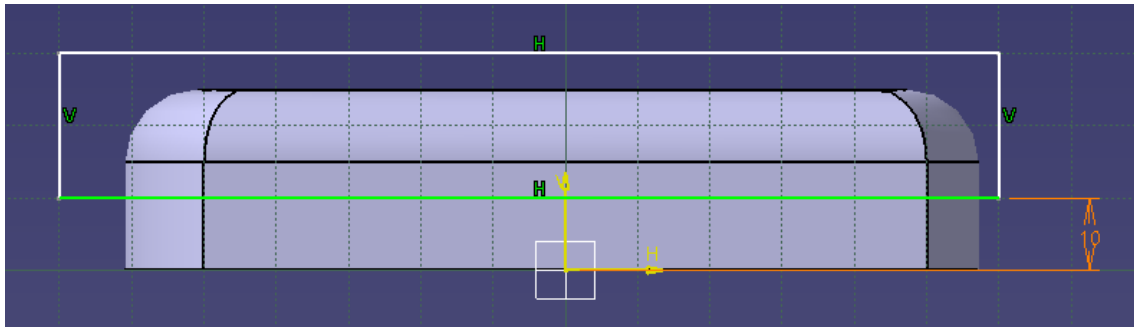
Pisador horizontal FUENTE: [Propia]
